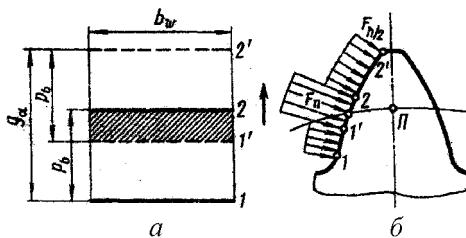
Схема однопарного и двухпарного зацепления зубьев
